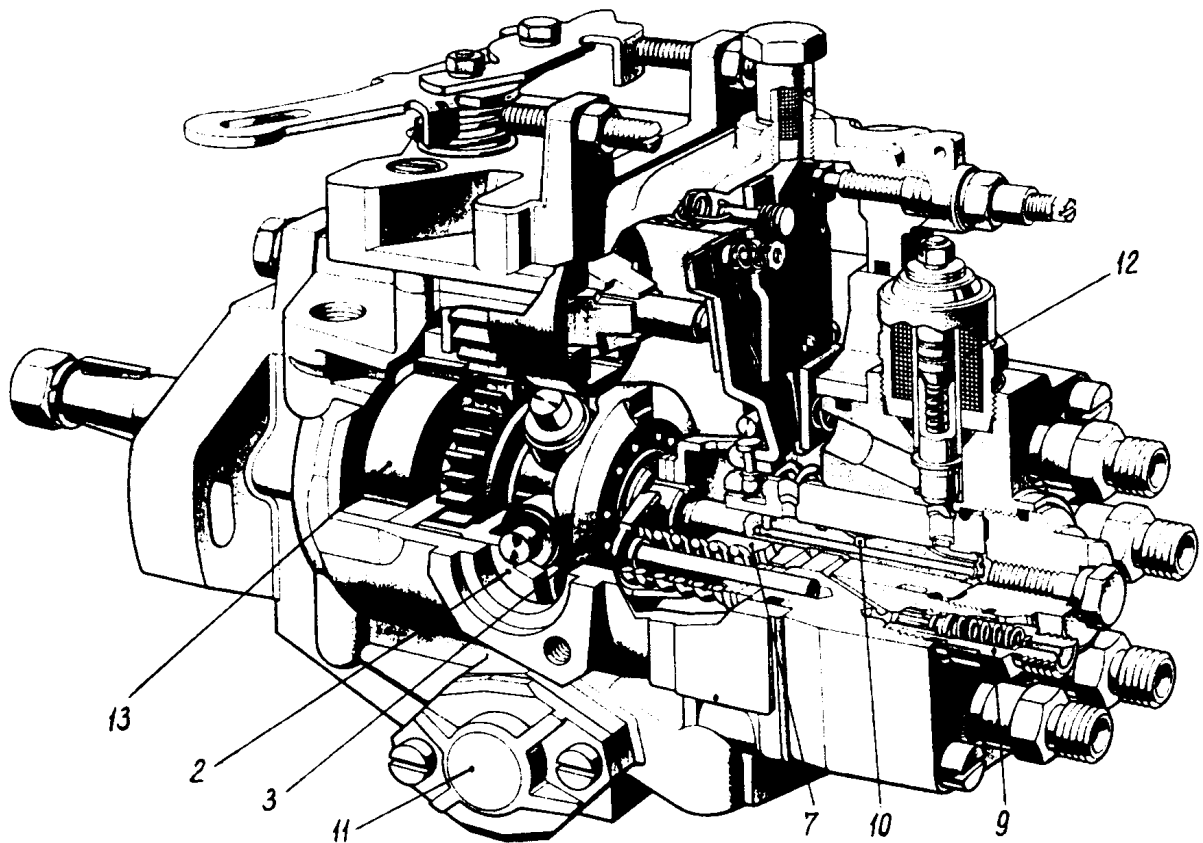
ПНВТ VE фірми "R.Bosch" базової конструкції з механічним регулятором
